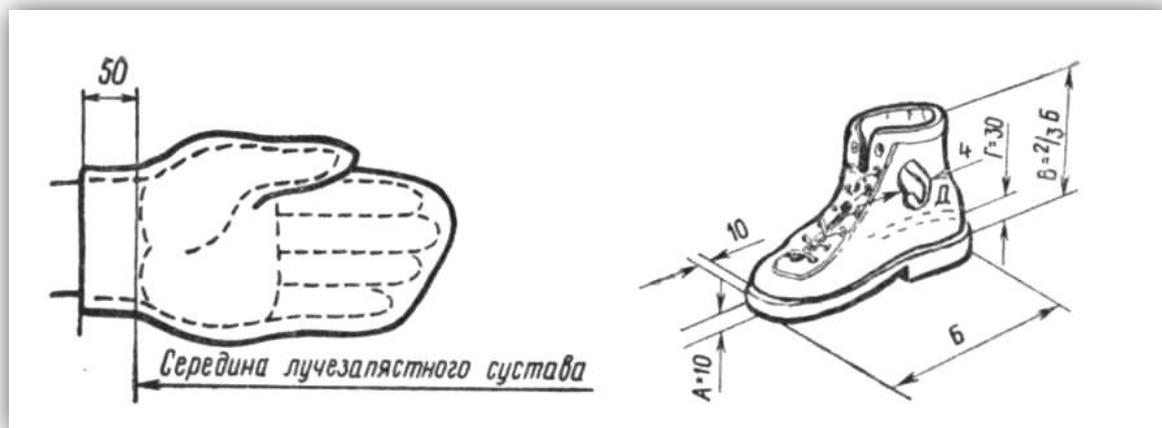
Рукавица (перчатка) для стрельбы из винтовки.
